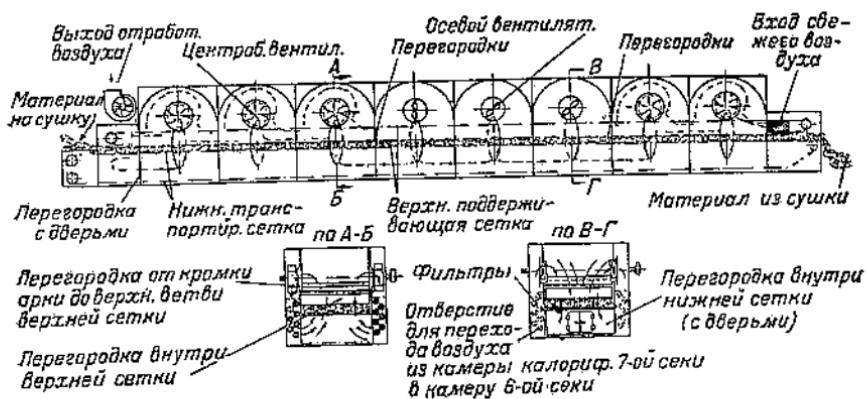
Ленточная сушилка для шерсти ЛС-1
